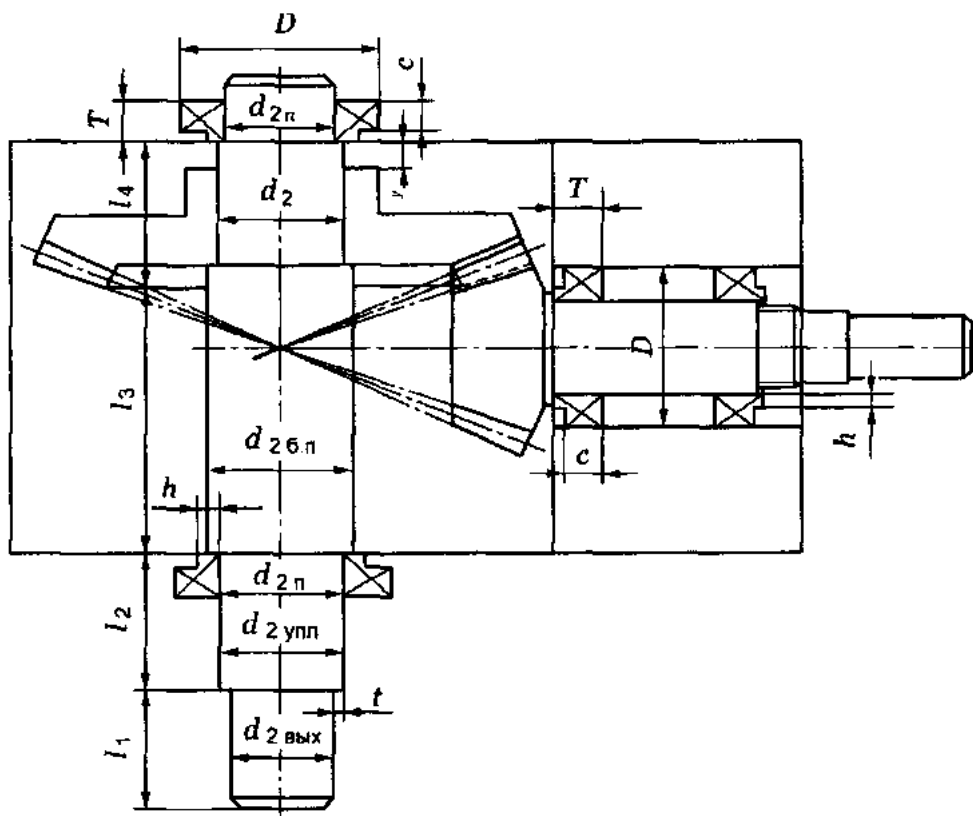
Эскиз конической передачи редуктора
